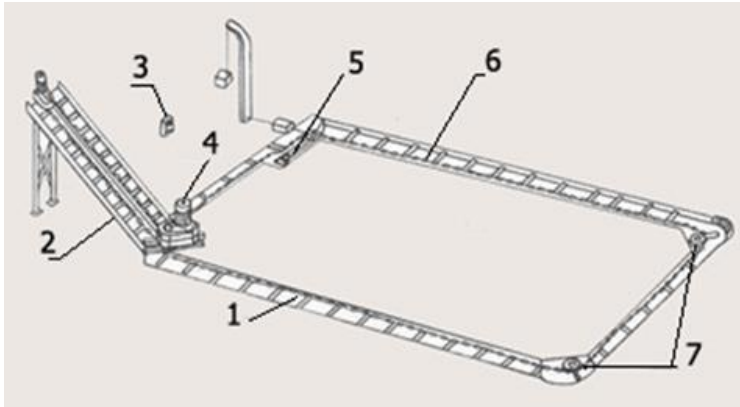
Схема конвеєра для видалення гною КСГ-7: 1 — горизонтальний конвеєр; 2 — похилий конвеєр; 3 — пульт керування; 5 — натяжний пристрій; 6 — ланцюг; 7 — напрямні зірочки
